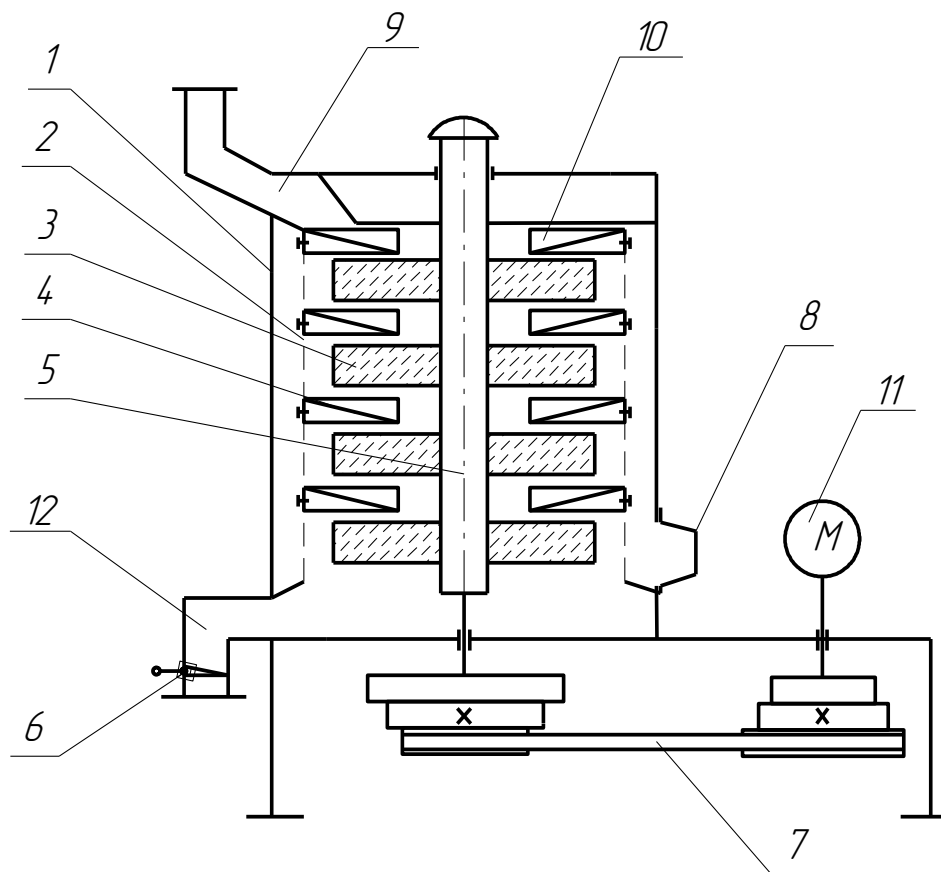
Луцильно-шліфувальна машина: 1 – корпус; 2 – сітка; 3 – диск; 4 – направляючий диск; 5 – вал; 6 – регулятор; 7 – привід; 8 – патрубок повітряний; 9 – завантажувальний патрубок; 10 – гонки; 11 – двигун; 12 – випускний патрубок.
